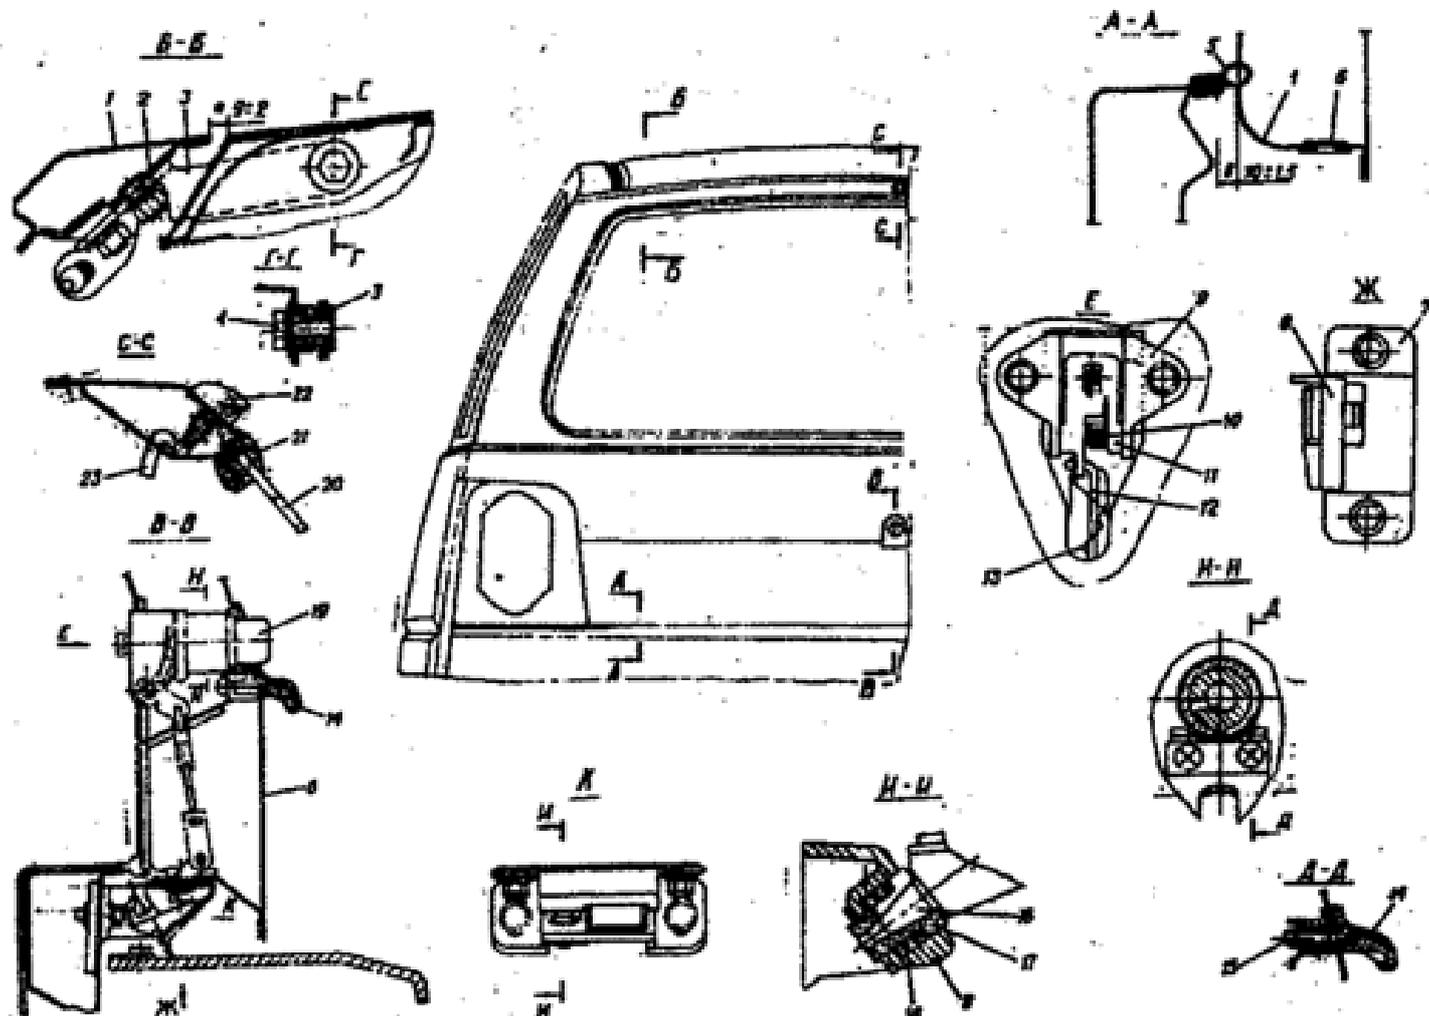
Арму́ра двери задка: 1 - дверь задка; 2 - гайка крепления петли; 3 - петля двери; 4 - болт крепления петли на кузове; 5 - уплотнитель двери задка; 6 - заглушка; 7 - замок двери задка; 8 - фиксатор замка; 9 - привод замка; 10 - пружина привода замка; 11 - рычаг привода; 12 - тяга привода; 13 - фиксатор тяги; 14 - ручка двери; 15 - винт крепления ручки; 16 - шип замка; 17 - направляющая втулка; 18 - пружина направляющей втулки; 19 - кнопка замка двери; 20 - стекло двери задка; 21 - уплотнитель стекла; 22 - жиклер стеклоомывателя; 23 - трубка подвода воды.
